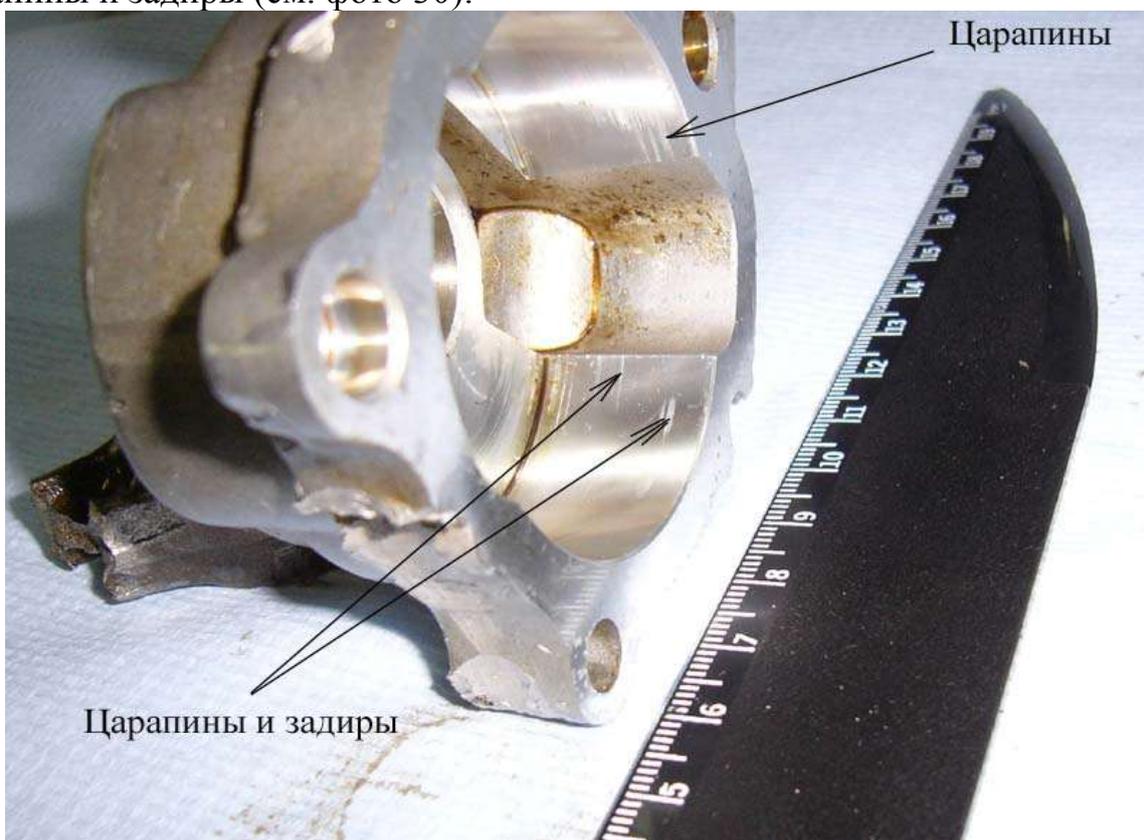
Повреждения внутренней поверхности корпуса масляного насоса.
